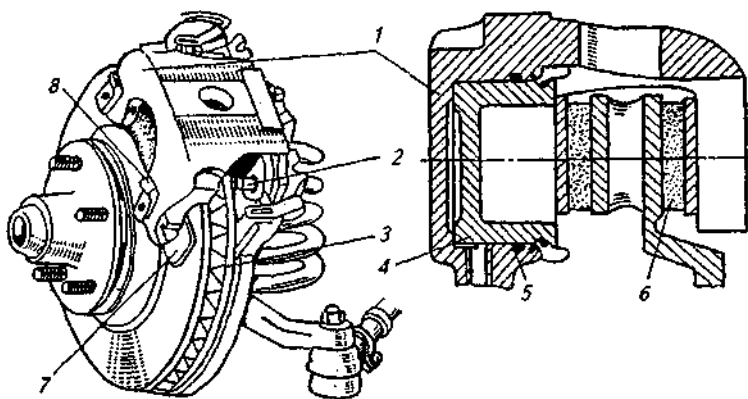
Дисковый тормозной механизм с плавающей скобой: 1 — скоба; 2 — направляющие штифты; 3 — суппорт; 4 — поршень; 5 — уплотнительное кольцо; 6, 7 — колодки; 8 — пластинчатая пружина
